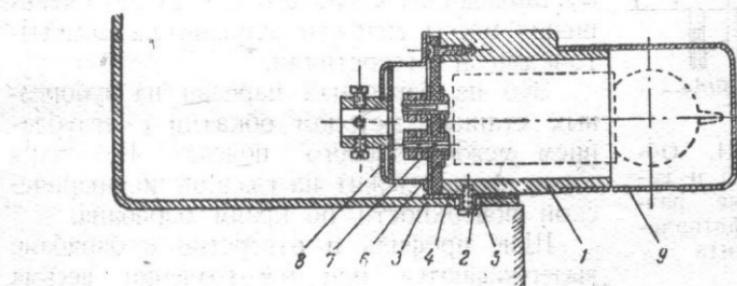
Фотоячейка: 1—корпус; 2—винты; 3—угольник; 4—прокладка; 5—втулки; 6—панель; 7—гнездо; 8—экранирующий колпачок; 9—колпачок
